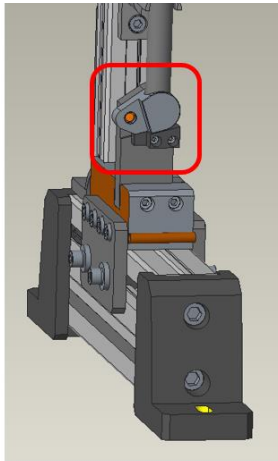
Colocador de soldadura antes do sistema de fixação ser alterado
